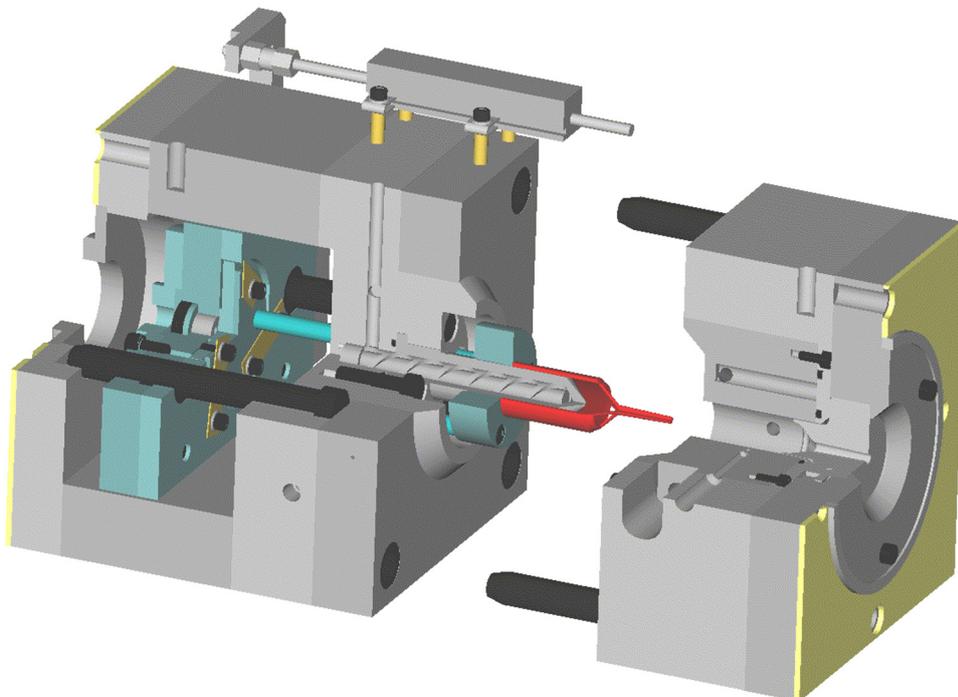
Werkzeug zur Entformungskraftmessung an hülsenförmigen Bauteilen /160//162/
